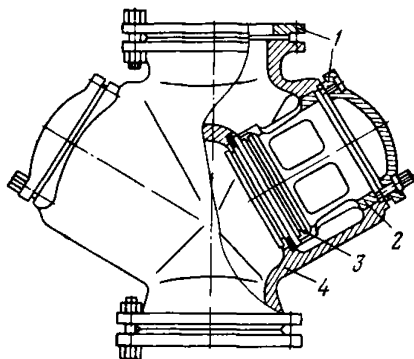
Обратный клапан компрессора 4BM10-100/8:
